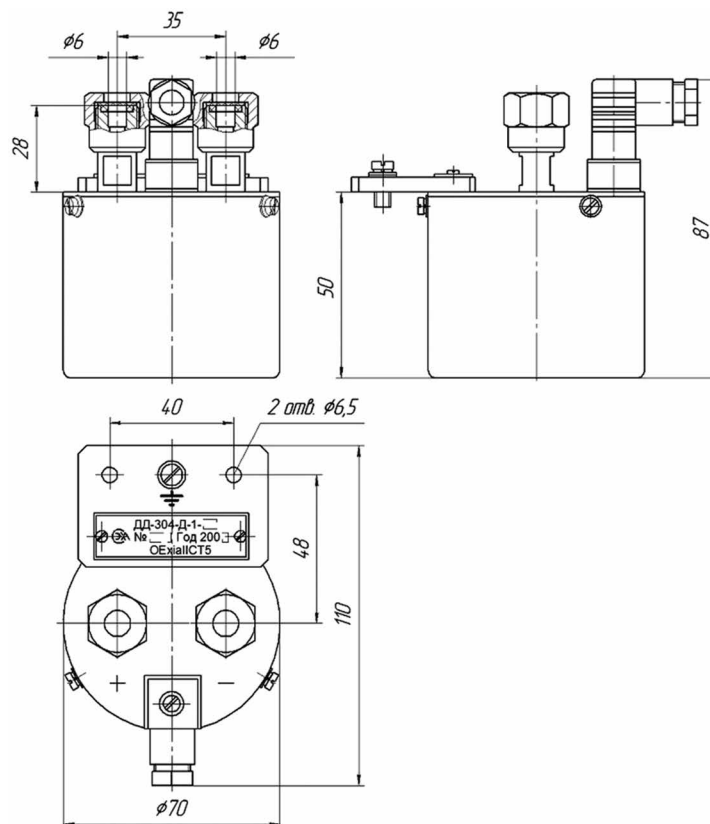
Габаритные и установочные размеры датчика перепада давлений ДД-304-Д-1
